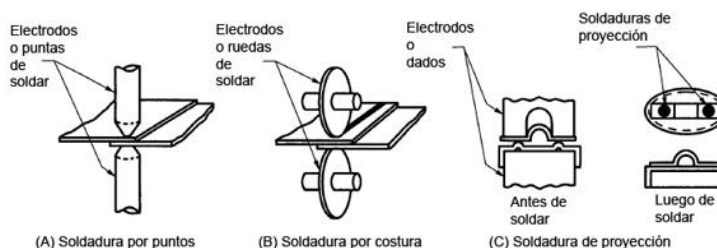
Bocetos de distintos tipos de Soldadura RW
